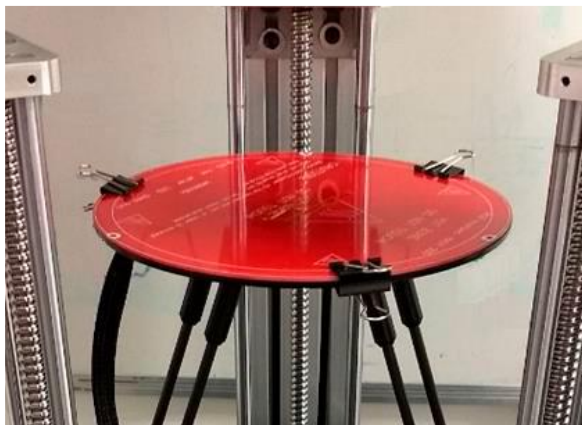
TwinTeeth PCB Mini-Factory. Fonte: [11]
